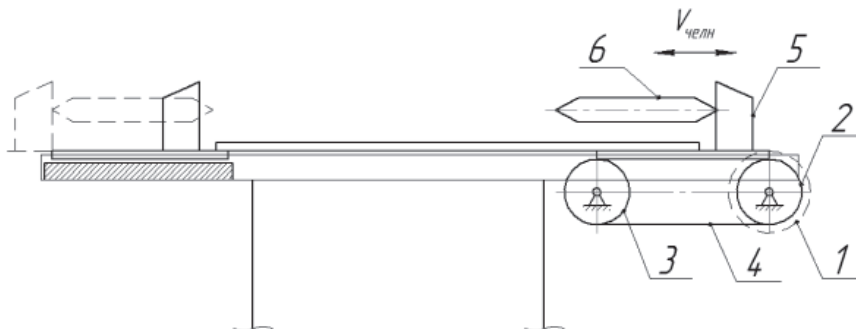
Общая схема конструкции боевого механизма станка для выработки технических тканей
